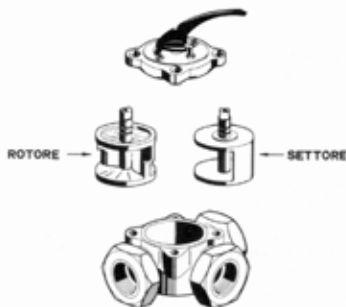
Esplosione valvola a 3 vie con interno a rotore o settore
